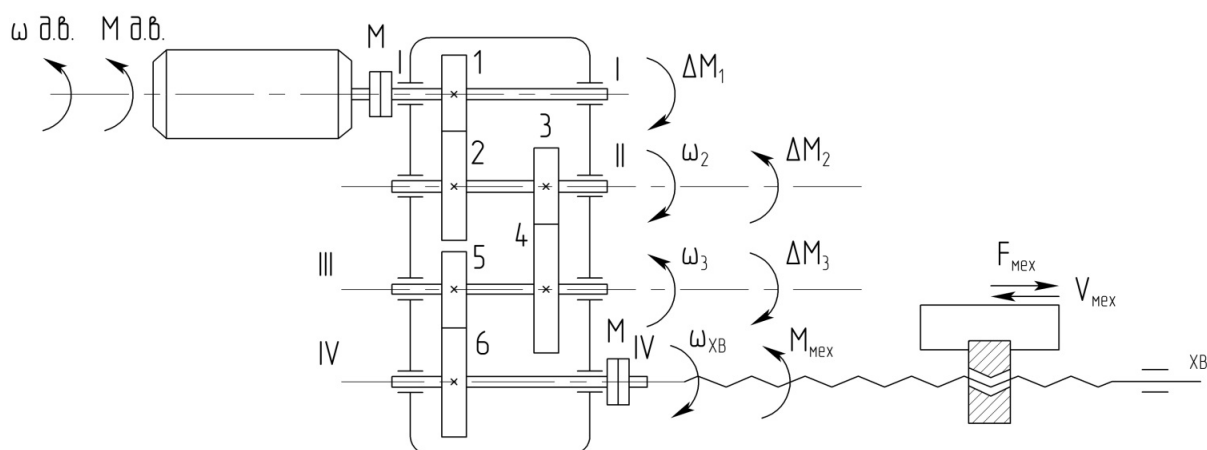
Кинематическая схема механической системы привода движения подачи металлорежущего станка
